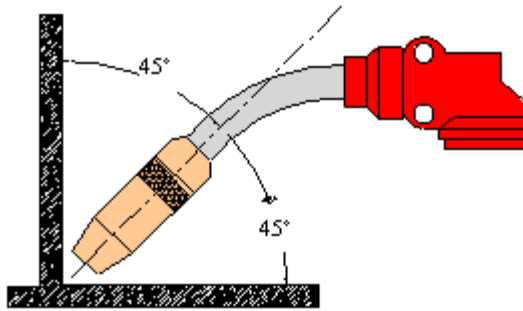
Posición de la pistola para soldadura de ángulo interior
